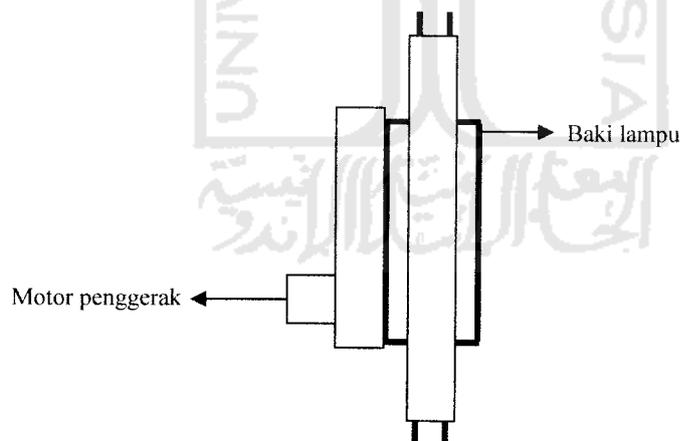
Penjepit elektroda lampu tampak samping depan
